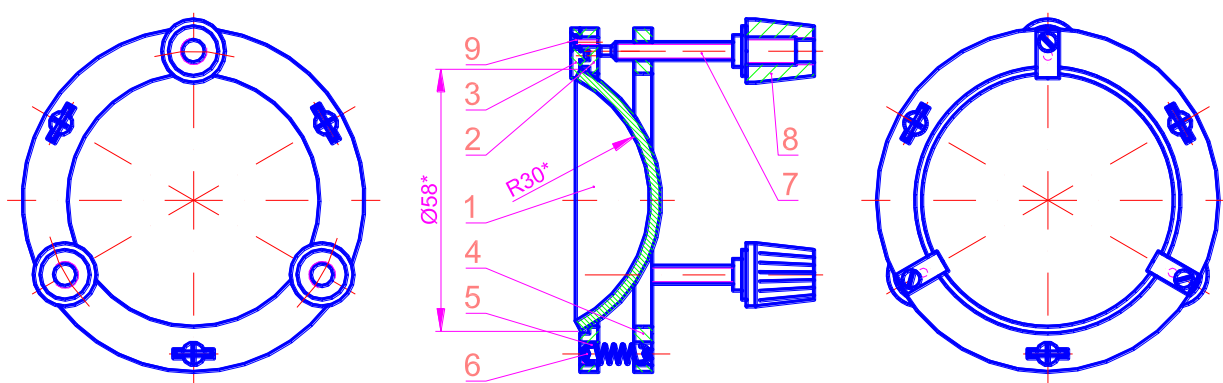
Проектування пристрою юстирування: 1 – дзеркало сферичне; 2 – оправка; 3 – планка; 4 – основа; 5 – пружина; 6 – вісь; 7 – гвинт юстирувальний; 8 – рукоятка; 9 – гвинт
